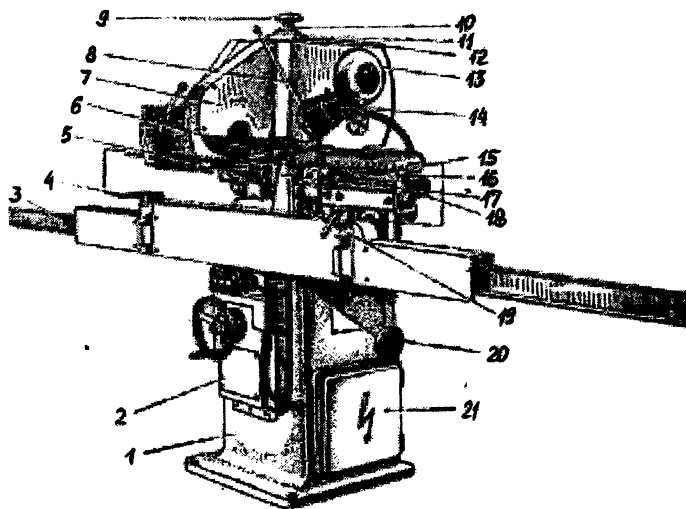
Станок TchPP-2 для заточки рамных пил
